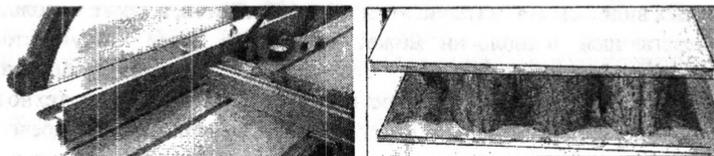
Изготовление торцового наполнителя на станке и склеенный щит
